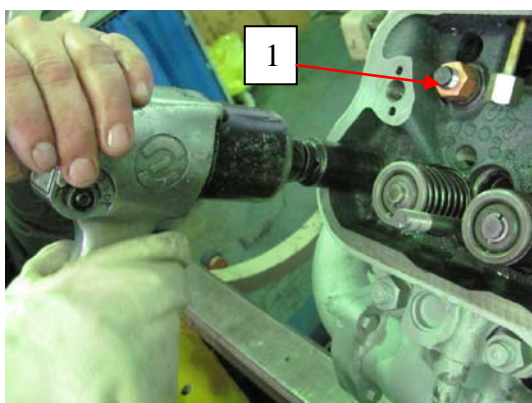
Отвернуть гайки. Снятие головки цилиндров.
